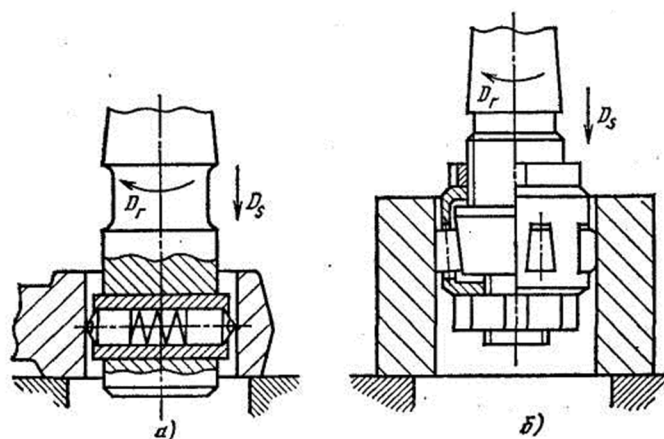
Схемы обработки отверстий выглаживанием и накатыванием
